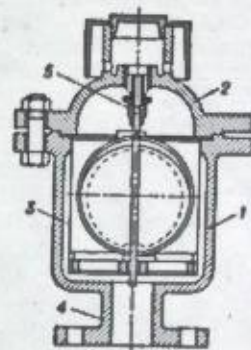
Воздушный вантуз: 1—корпус; 2—крышка; 3—сетка; 4—патрубок; 5—клапан.
